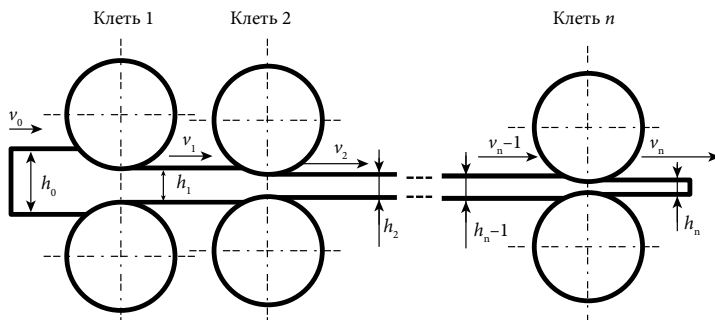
Схема деформации заготовки в чистой группе клетей непрерывного широкополосового стана
